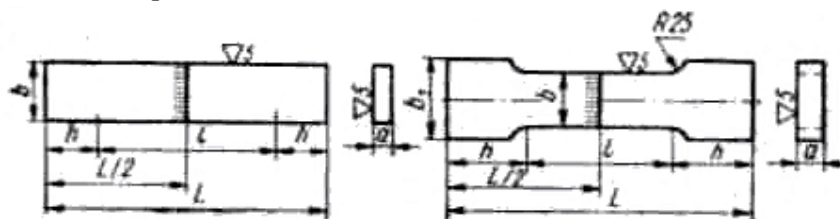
Форма образцов для испытания сварного соединения на статическое растяжение
